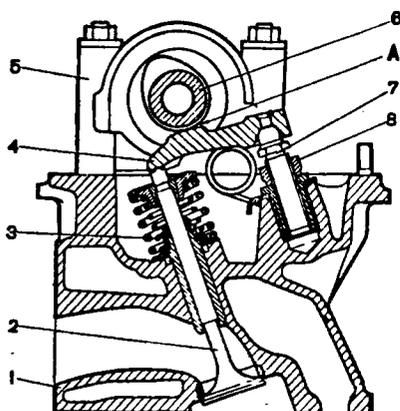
Разрез головки цилиндров по выпускному клапану: 1 - головка цилиндров; 2 - выпускной клапан; 3 - маслоотражательный колпачок; 4 - рычаг клапана; 5 - корпус подшипников распределительного вала; 6 - распределительный вал; 7 - регулировочный болт; 8 - контргайка болта; А - зазор между рычагом и кулачком распределительного вала
